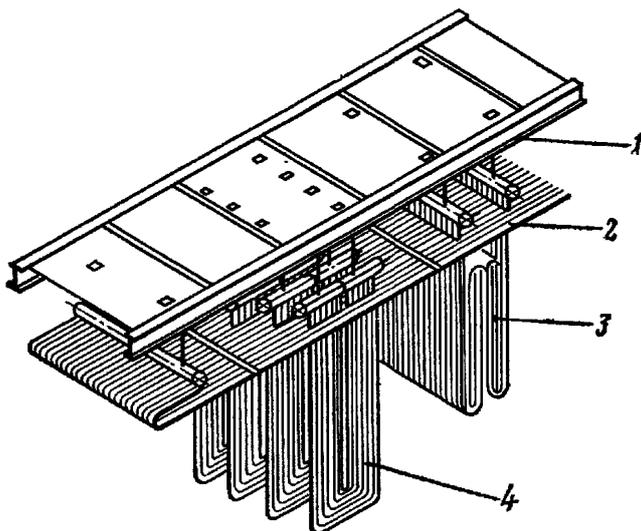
Блок потолочного перекрытия с поверхностями нагрева
